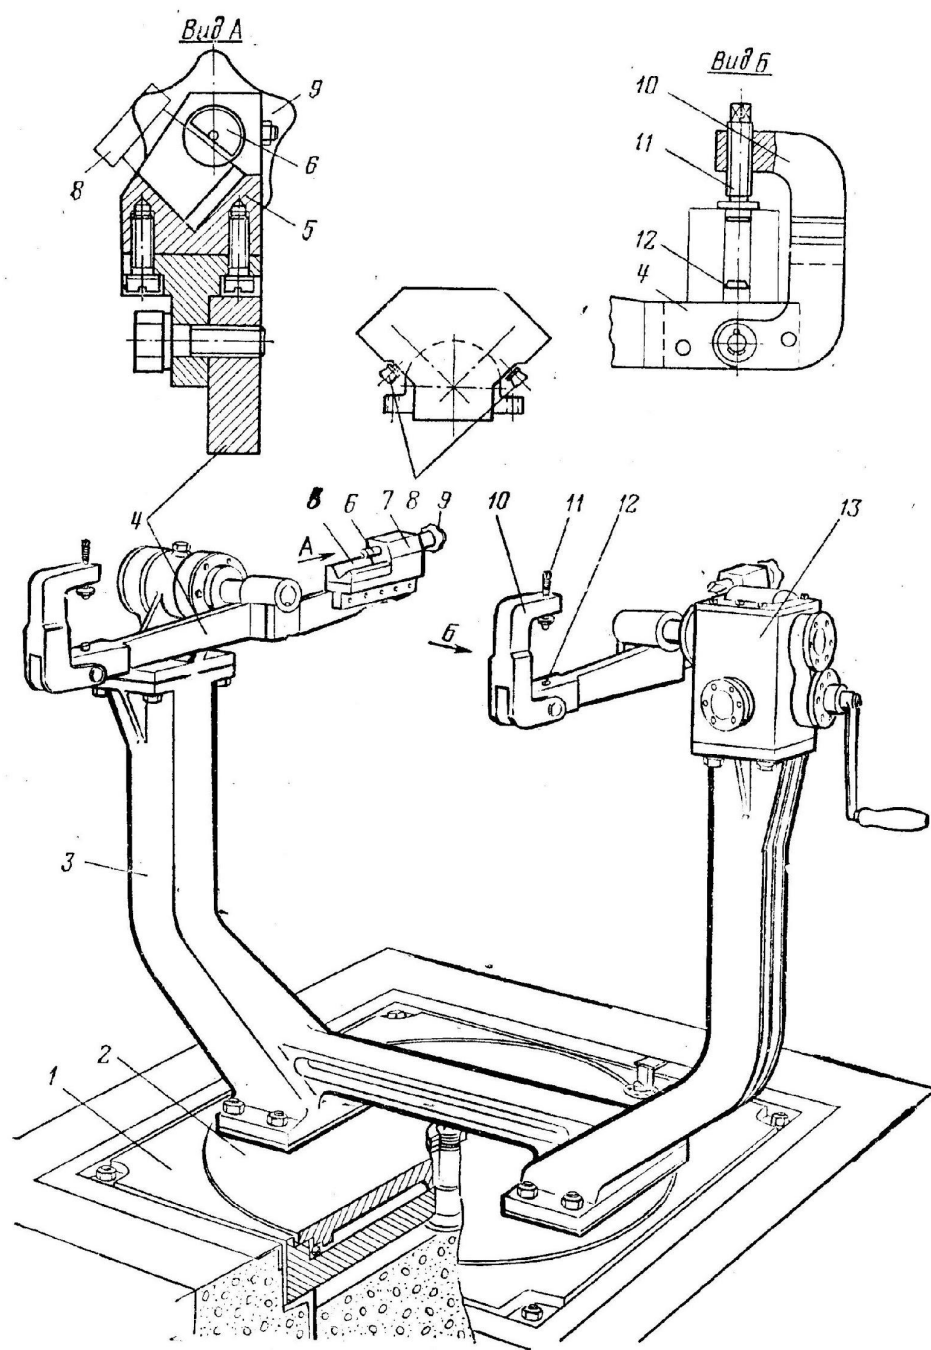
Стенд для разборки (сборки) двигателей ЗИЛ-130
